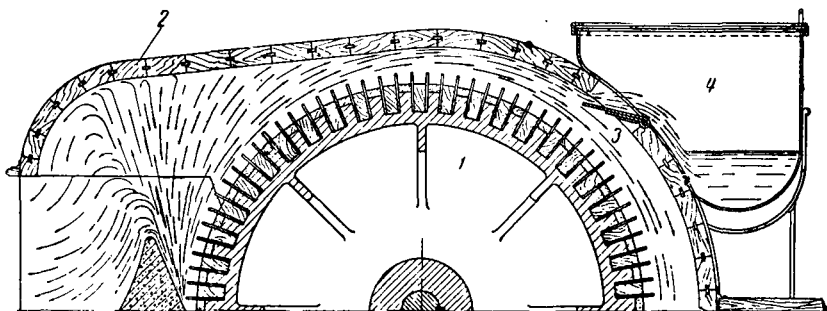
Установка желоба для отбора массы, перебрасываемой через барабан:
